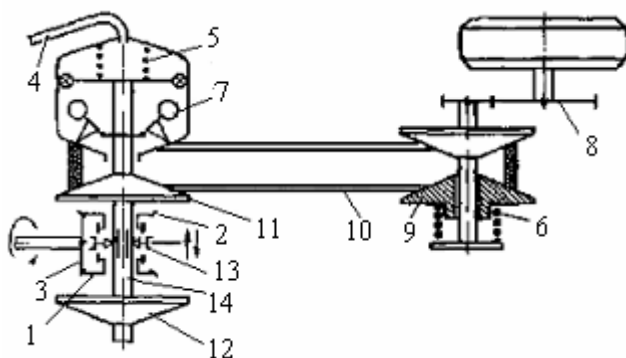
Клинопасова безступінчатa коробка передач:
